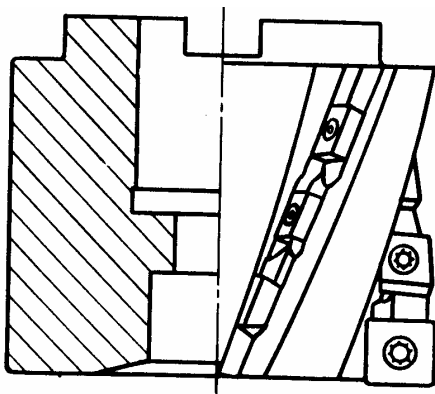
Торцева насадна фреза з квадратними пластинами, що чергуються від зуба до зуба в шаховому порядку
